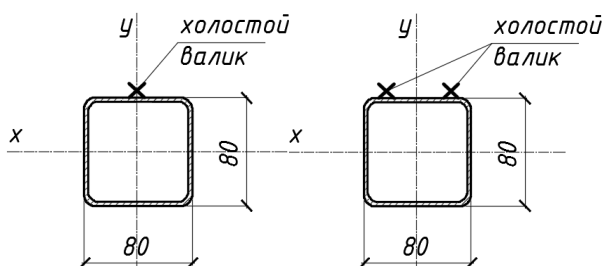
Схемы наплавки одного и двух холостых валиков по одной из главных осей стальных конструкций из труб квадратного сечения
